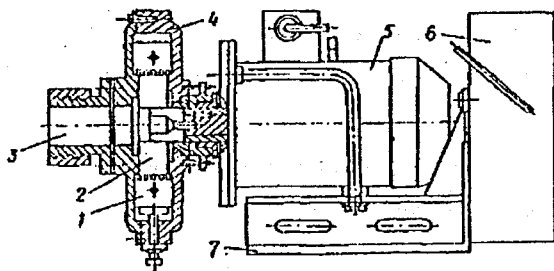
Диспергатор СО-128: 1 - башмак; 2 - ротор; 3 - завантажувальний патрубок; 4 - корпус; 5 - електродвигун; 6 - електрошафа; 7 - рама
